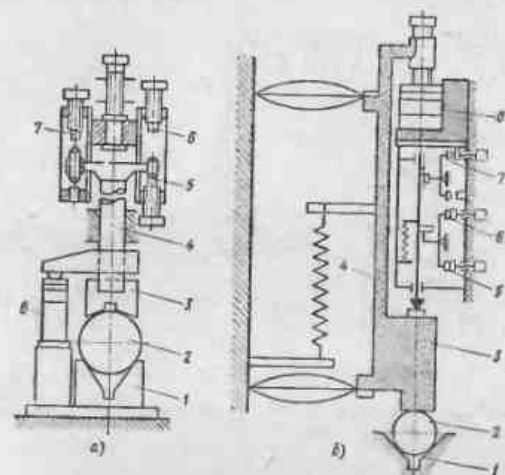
Схема контроля диаметра и огранки: а — с параллельным расположением детали и блока концевых мер; б — с последовательным расположением
